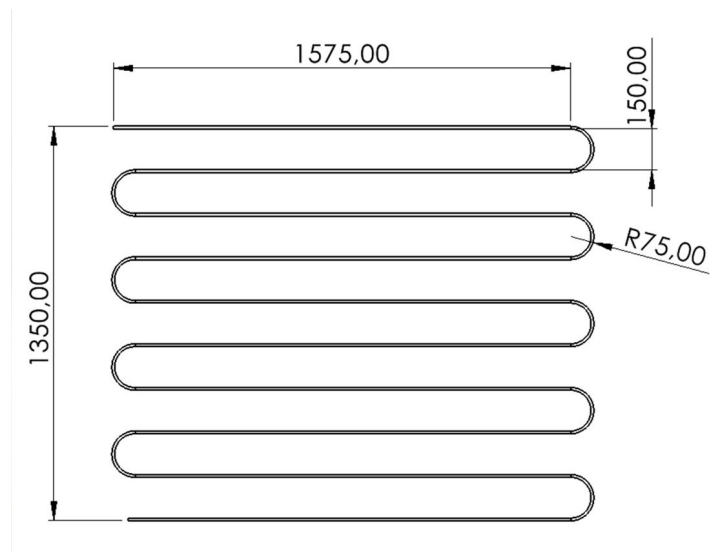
Dimensões da serpentina de tubos de cobre de 3/8".
